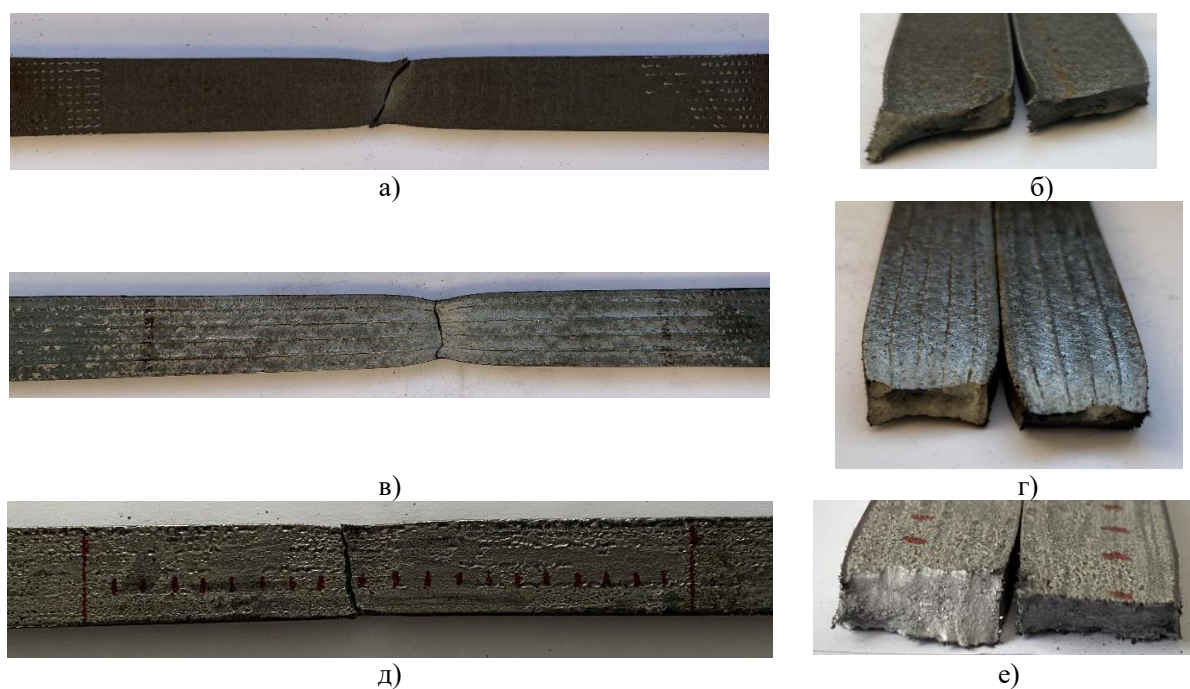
Разрушенные образцы (а, в, д) и сечение разрушения (б, г, е): а, б – образец НО2; в, г – образец 1б; д, е – образец ба
